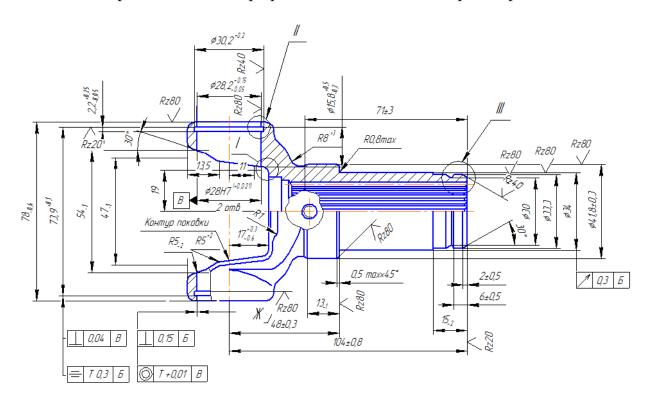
Рабочий чертеж вилки карданного вала LADA 4x4 Urban
